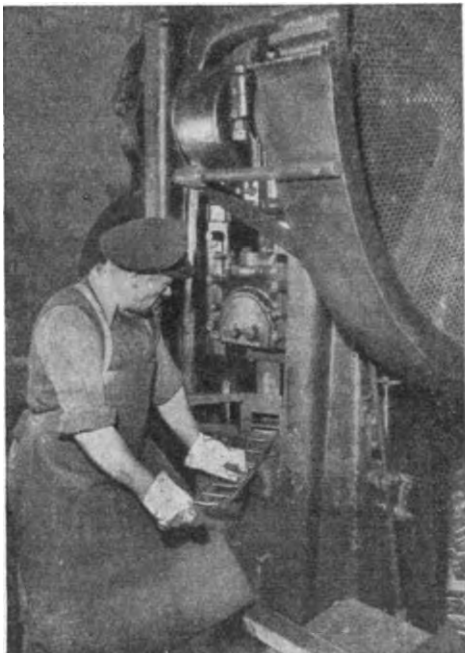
Eindringen der Magnetkerne auf dem Balancier
